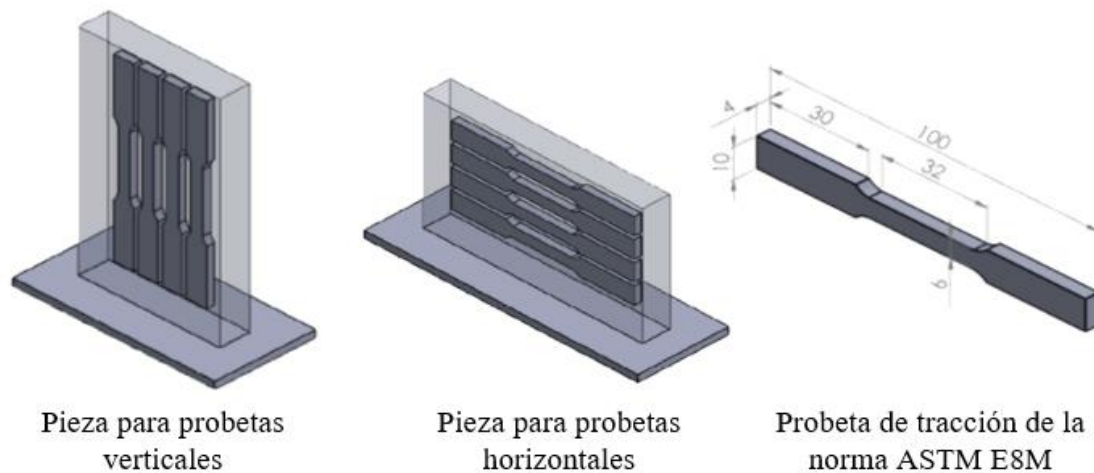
Configuración de extracción de las probetas de tracción de las piezas fabricadas.
